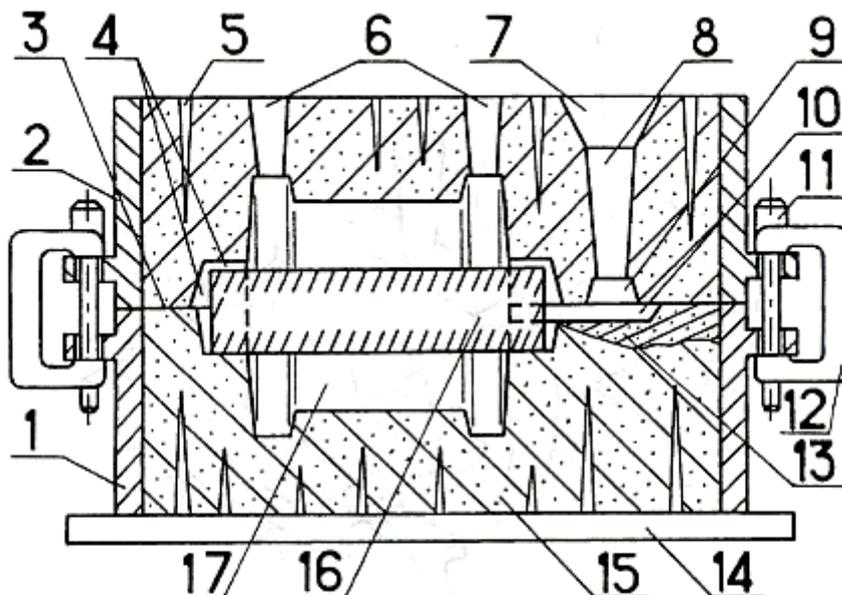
Эскиз песчаной литейной формы в сборе: 1 - нижняя опока; 2 - верхняя опока; 3 - плоскость разреза; 4 - зазоры; 5 - вентиляционный канал; 6 - выпоры; 7 - литниковая чаша; 8 - стояк; 9 - шлакоуловитель; 10 - питатель; 11 - центрирующий штырь; 12 - скоба; 13 - местный разрез; 14 - плита; 15 - формовочная смесь; 16 - стержень; 17 - рабочая полость формы
